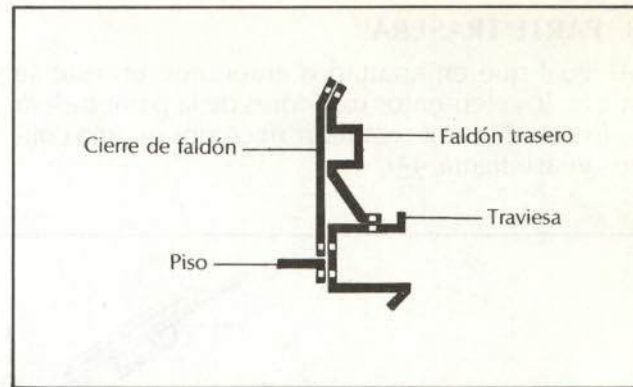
Sección del conjunto faldón-travesía-cierre.
